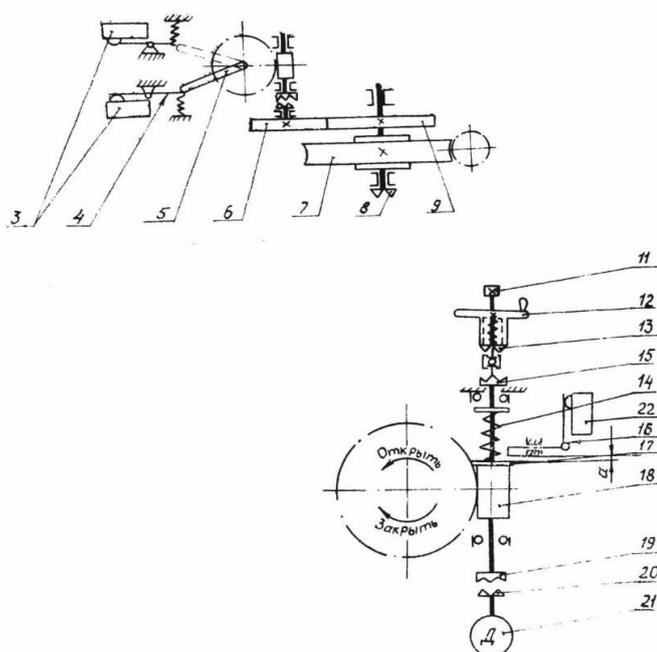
Кинематическая схема приводов общего назначения типов Б, В, Г
